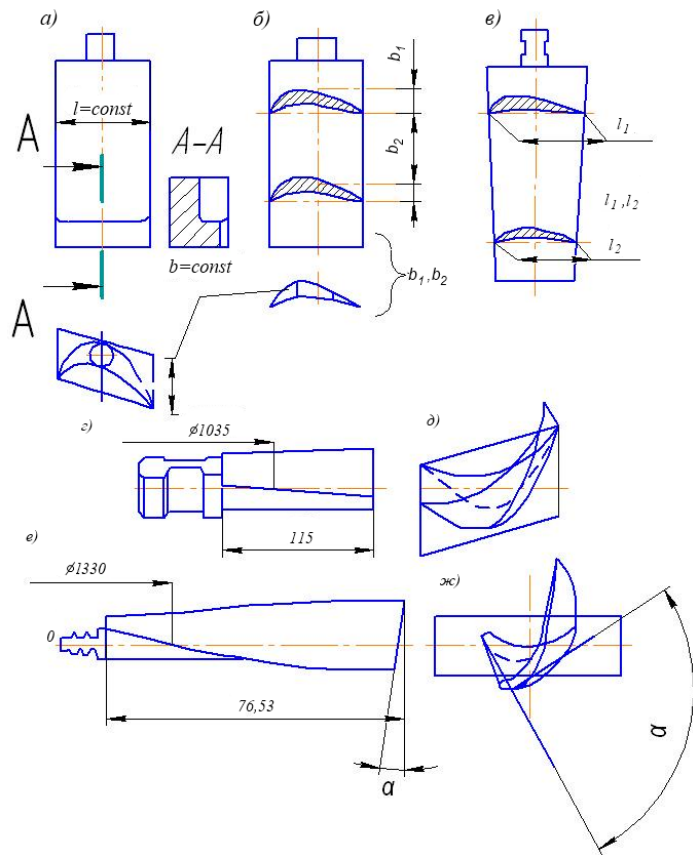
Фрагменты профилей обрабатываемых поверхностей лопаток турбин
